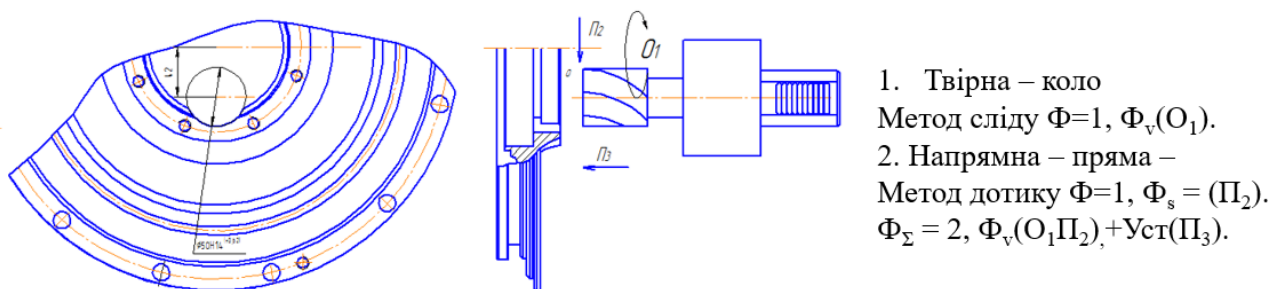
Формуючі рухи при обробці пазу фрезою
